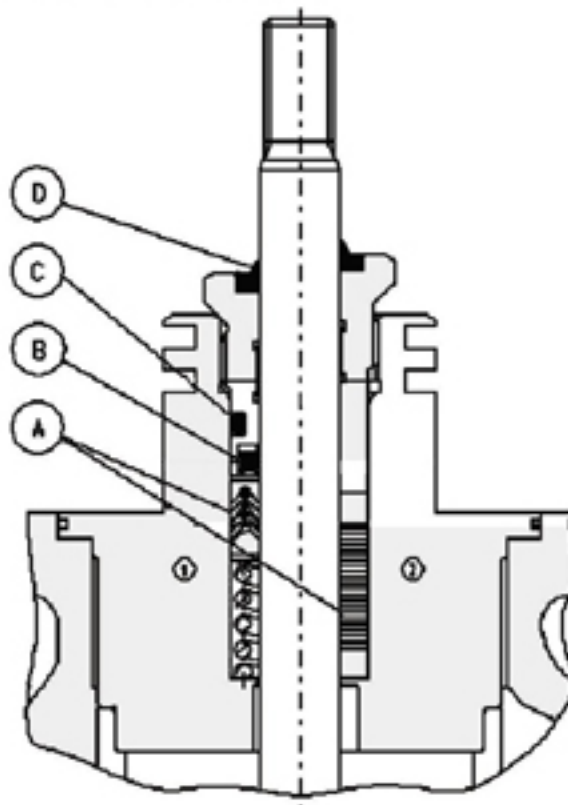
本体部构造 Fig.3 BODY SECTION VIEW
